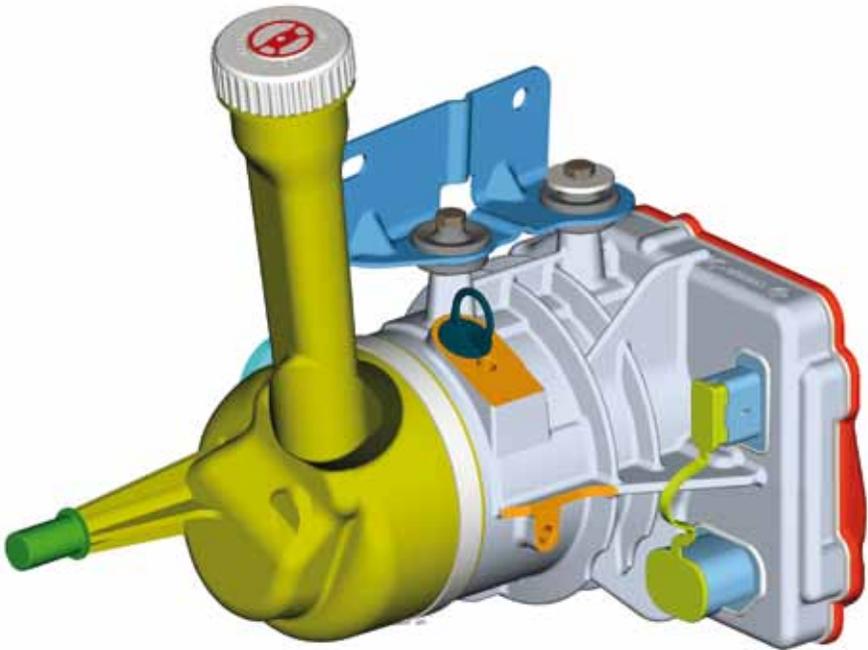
Das Motorpumpenaggregat liegt in einem Aluminium-Druckgussgehäuse. Plasmareinigung und -beschichtung bewirken die Leckage freie Haftung des Klebstoffs.
